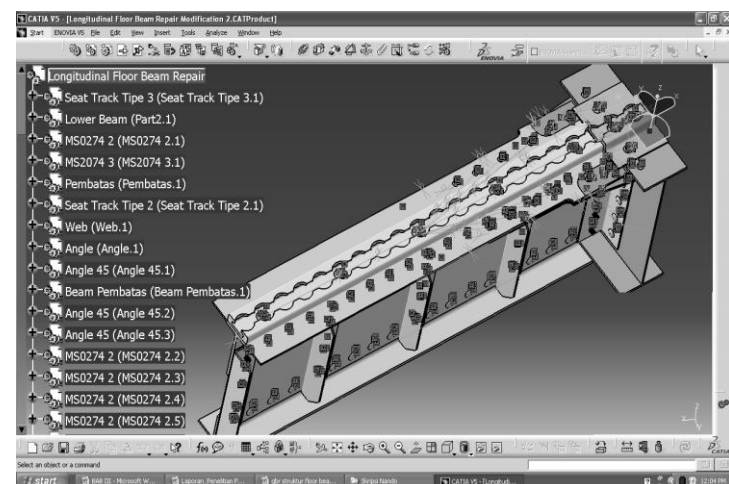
Model 1 Struktur *longitudinal floor beam* yang mengalami retak
